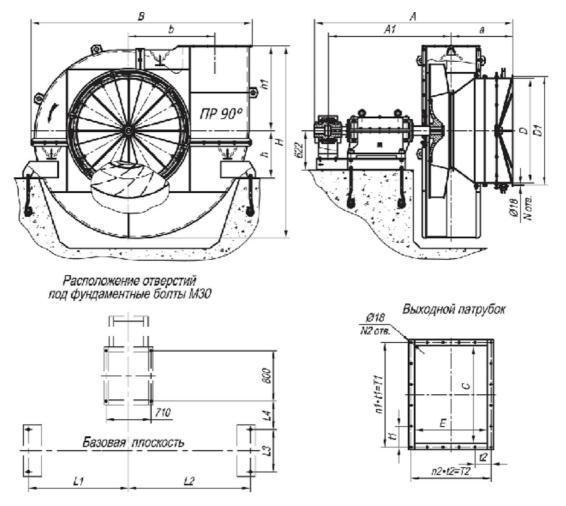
Габаритные и присоединительные размеры тягодутьевых машин типа ВДН и ДН №19-22 исп-3.
